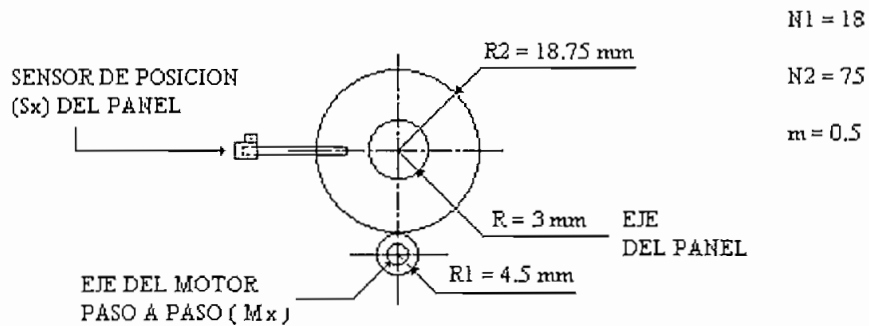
Grupo de engranajes acoplados al motor Mx
